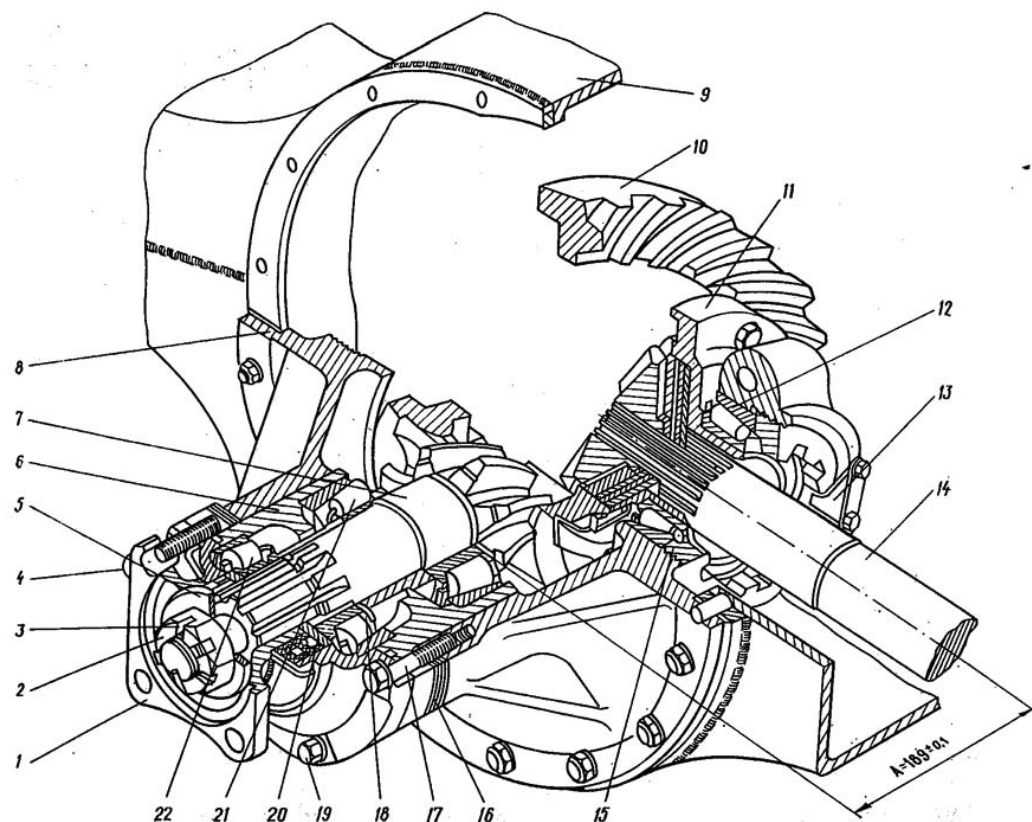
Регулировка главной передачи: 1 — фланец; 2 — гайка; 3 — шплинт; 4, 17, 19 — болт; 5 — шайба; 6 — стакан; 7 — шестерня ведущая; 8 — корпус главной передачи; 9 — корпус моста; 10 — шестерня ведомая; 11 — дифференциал; 12, 21, 22 — подшипник; 13 — крышка подшипника; 14 — полуось; 15 — гайка регулировочная; 16, 18 — прокладка регулировочная; 20 — крышка
